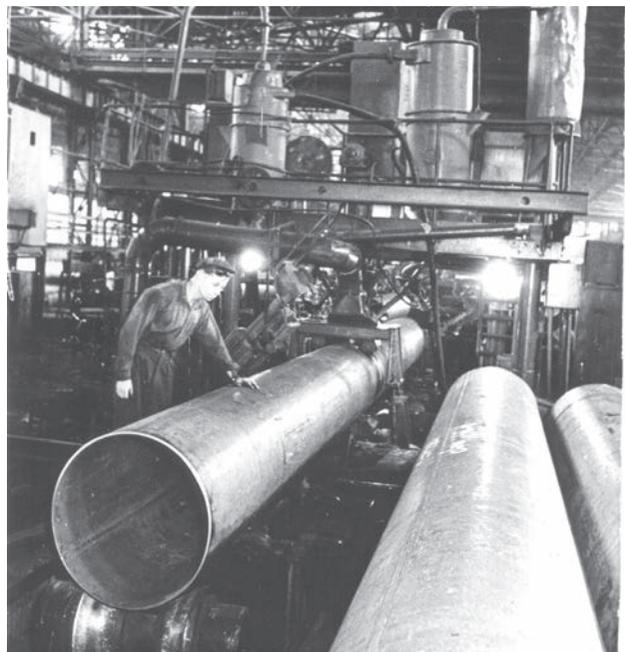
Цех автоматической сварки Харцызского трубного завода
